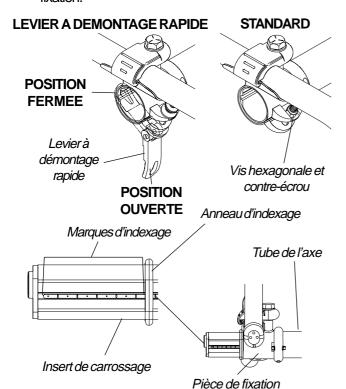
AJUSTER LA VOIE ARRIERE
